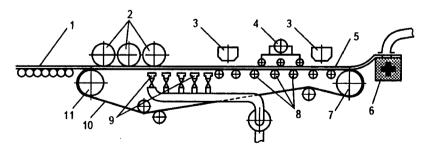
Схема работы плоскосетчатой машины для полусухого формования: 1 – роликовый конвейер; 2 – прессующие валки; 3 – посыпочные бункера; 4 – вибромеханизм; 5 – поддерживающие валки; 6 – приемная ванна; 7 – приводной вал; 8 – малые валки; 9 – вакум-коробка; 10 – сетчатое полотно; 11 – натяжной вал
